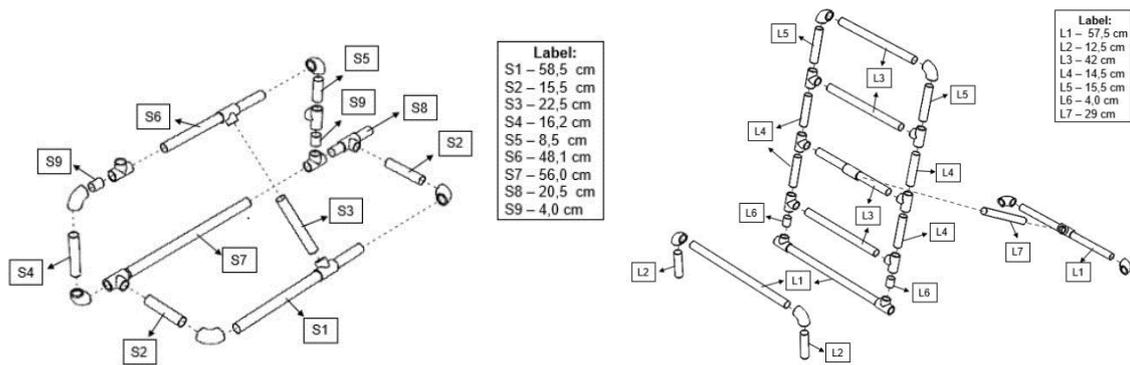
Desenho esquemático das partes separadas da lateral e do encosto para facilitar a construção do instrumento.
